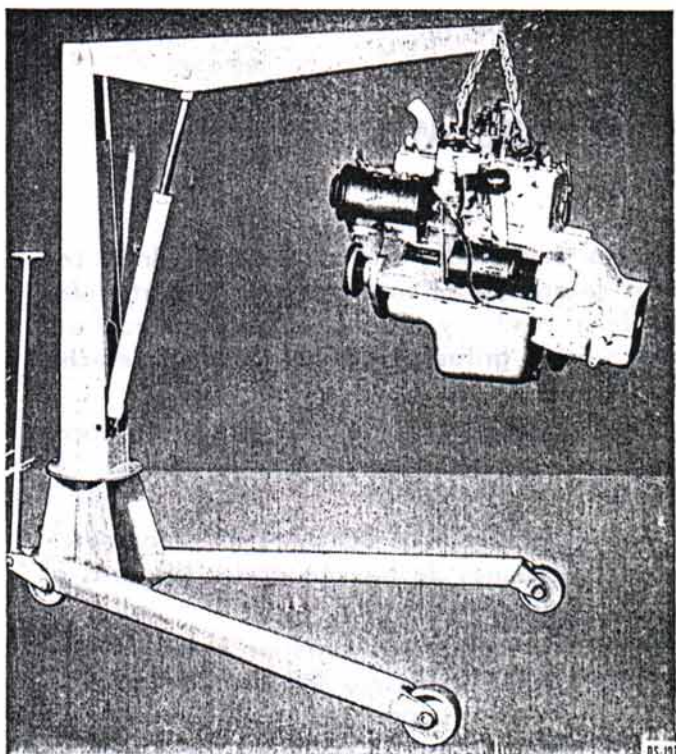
Guinche para instalar y extraer el motor del vehículo.
